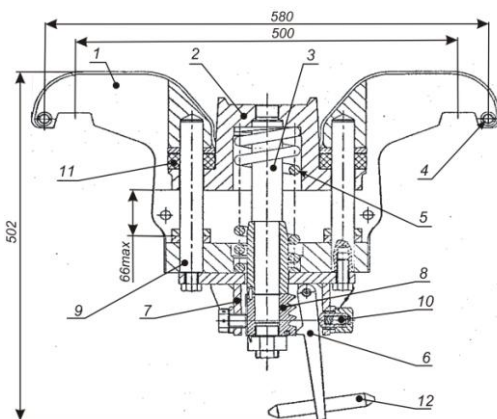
Схема центрирующего прибора с центрирующей балочкой оригинальной конструкции:
